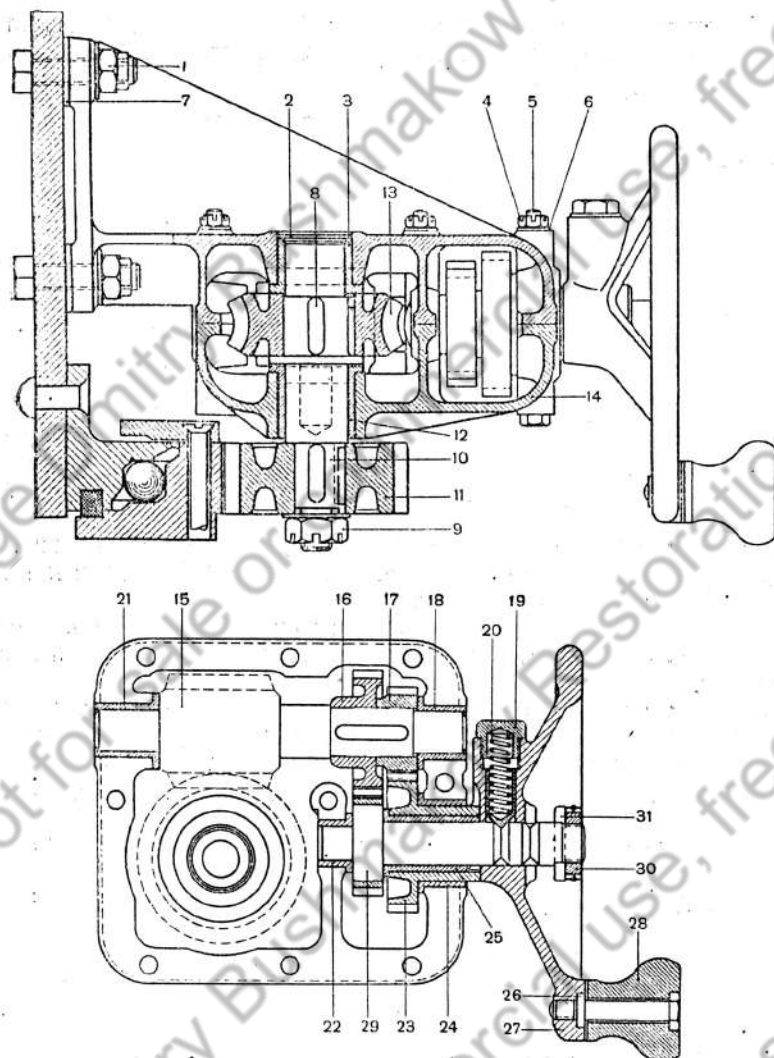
Поворотный механизм башни с 45-мм пушкой.
